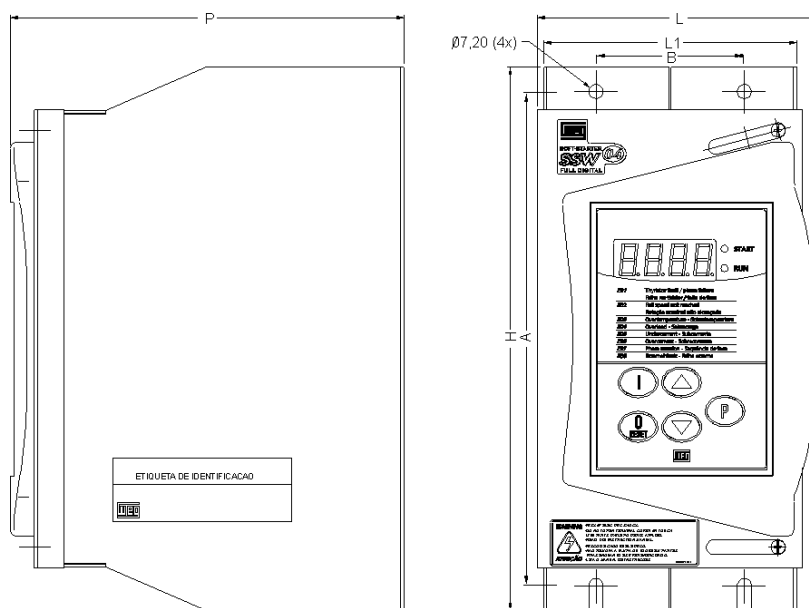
Dimensional da SSW-04 e furação para fixação
